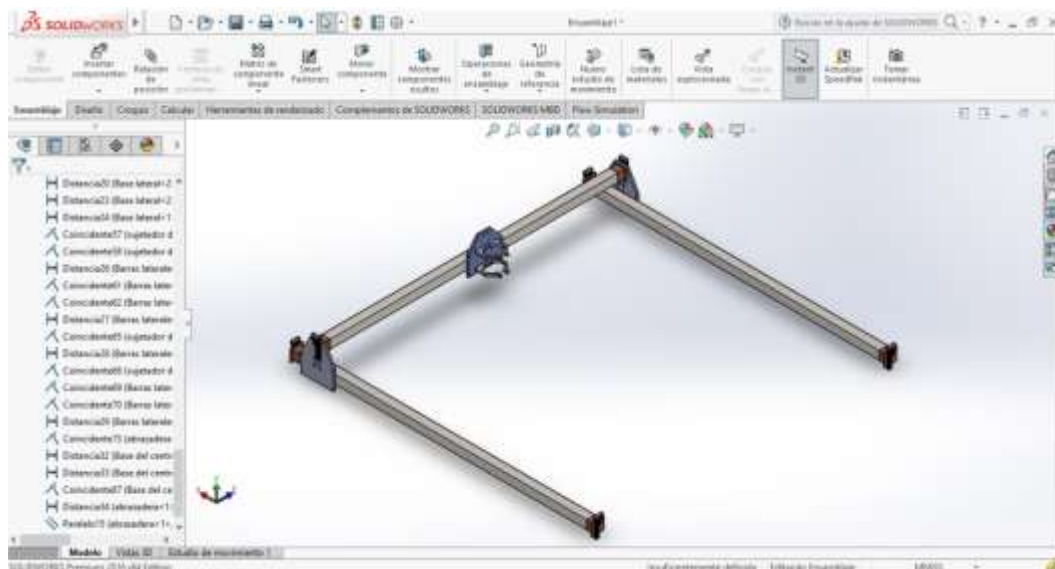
Ensamble final de la CNC diseñado en SolidWorks.
